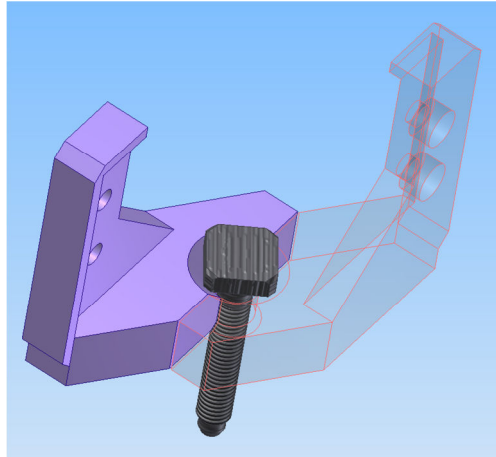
Detalhe das pinças com o parafuso em posição para ser largado [imagem fotorealista]
